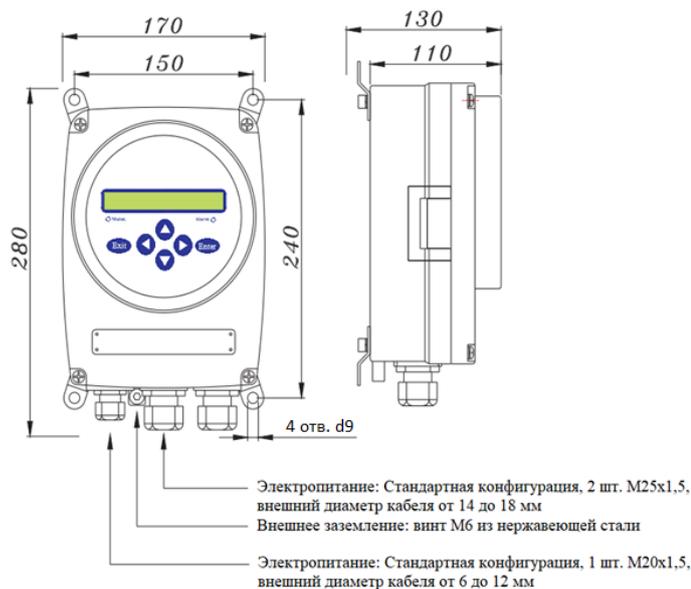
Размеры установки модуля на подвесное крепление
